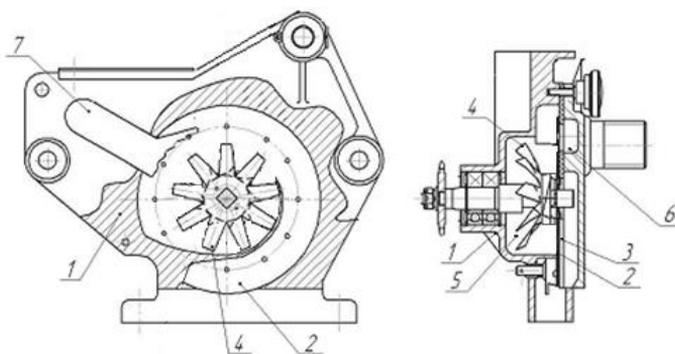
Схема вакуумного высевающего аппарата с предложенным ворошителем семян: 1 – корпус; 2 – высевающий диск; 3 – прокладка; 4 – предлагаемый ворошитель семян; 5 – семенная камера; 6 – вакуумная камера; 7 – сбрасыватель «лишних» семян
